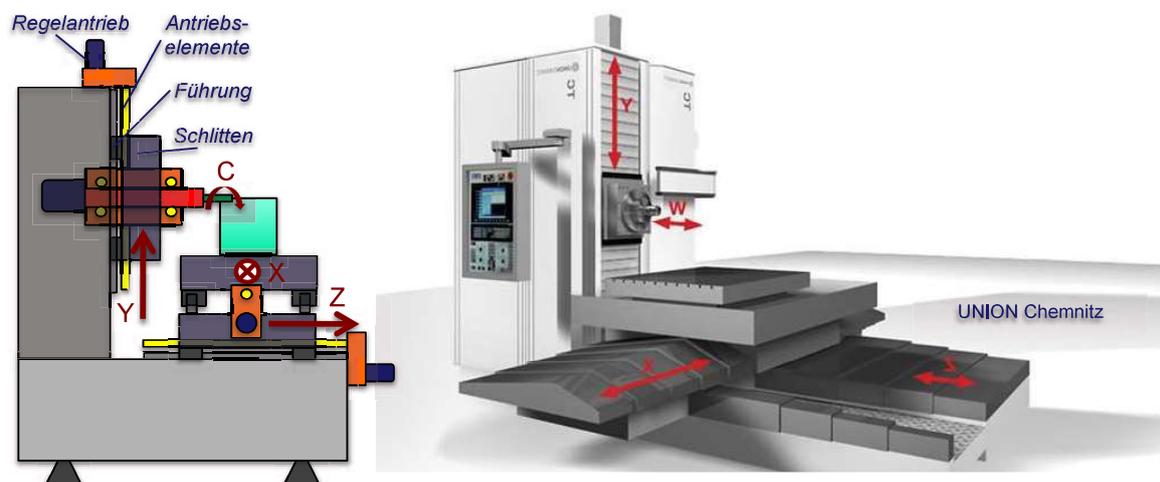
Einständer-Horizontal-Fräsmaschine
